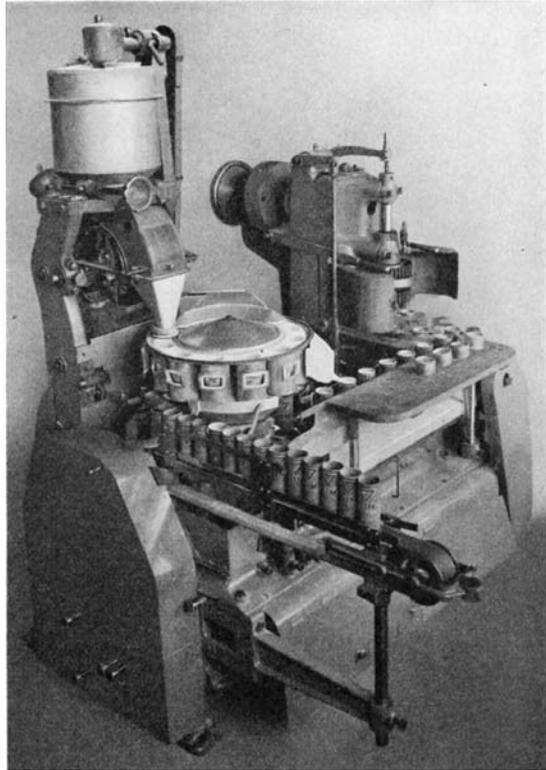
Selbsttätige Dosiermaschine (Fr. Hesser, Maschinenfabrik A G., Stuttgart-Cannstatt).
